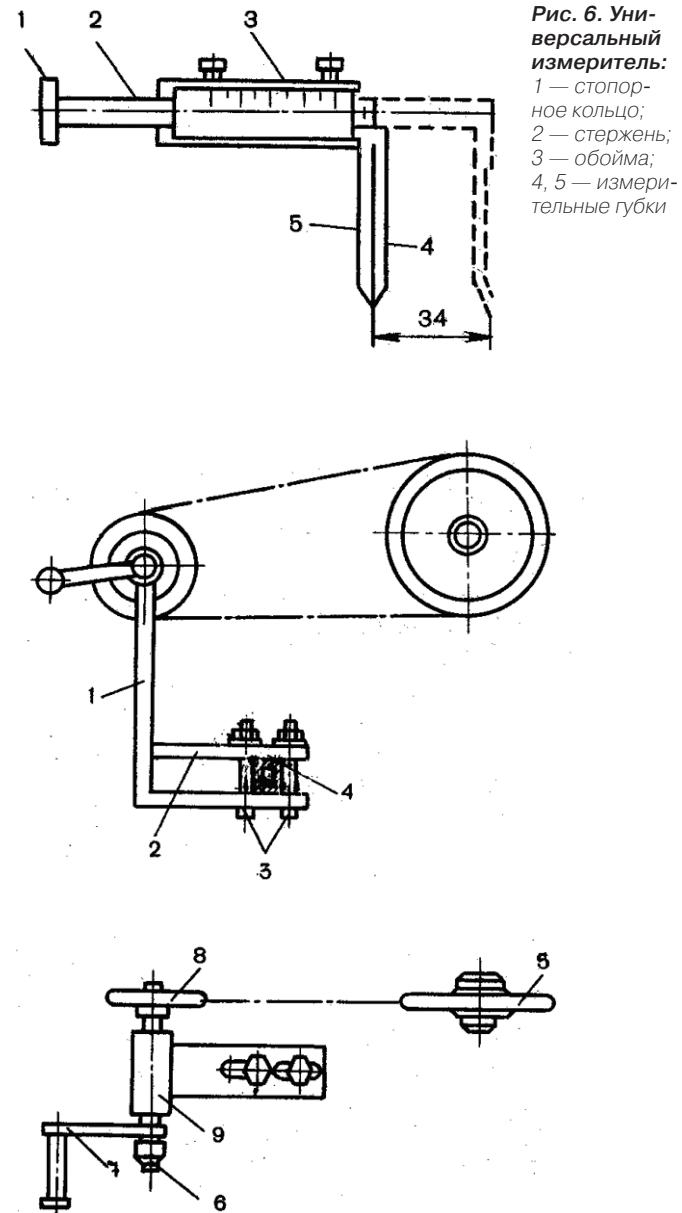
Приспособление для прокручивания вала высевающих аппаратов сеялок: 1 — кронштейн; 2 — пластины; 3 — болты; 4 — рама сеялки; 5 — втулка; 6 — валик; 7 — рукоятка; 8, 9 — звездочки
